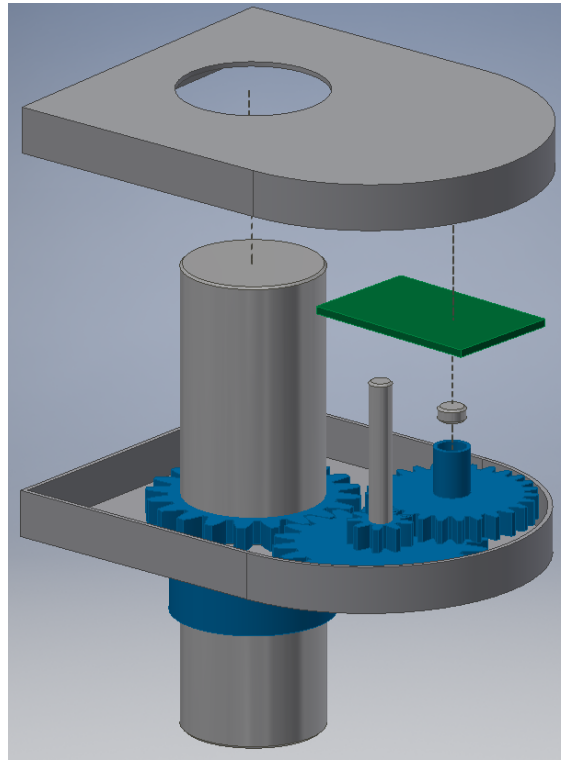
Montaje preliminar de sensor en pcb con imán y adaptación mecánica
